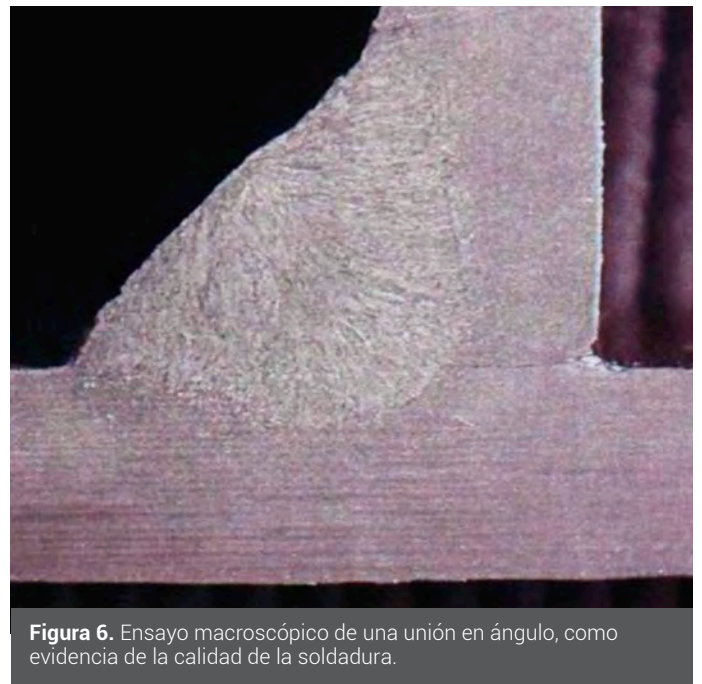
Ensayo macroscópico de una unión en ángulo, como evidencia de la calidad de la soldadura.
